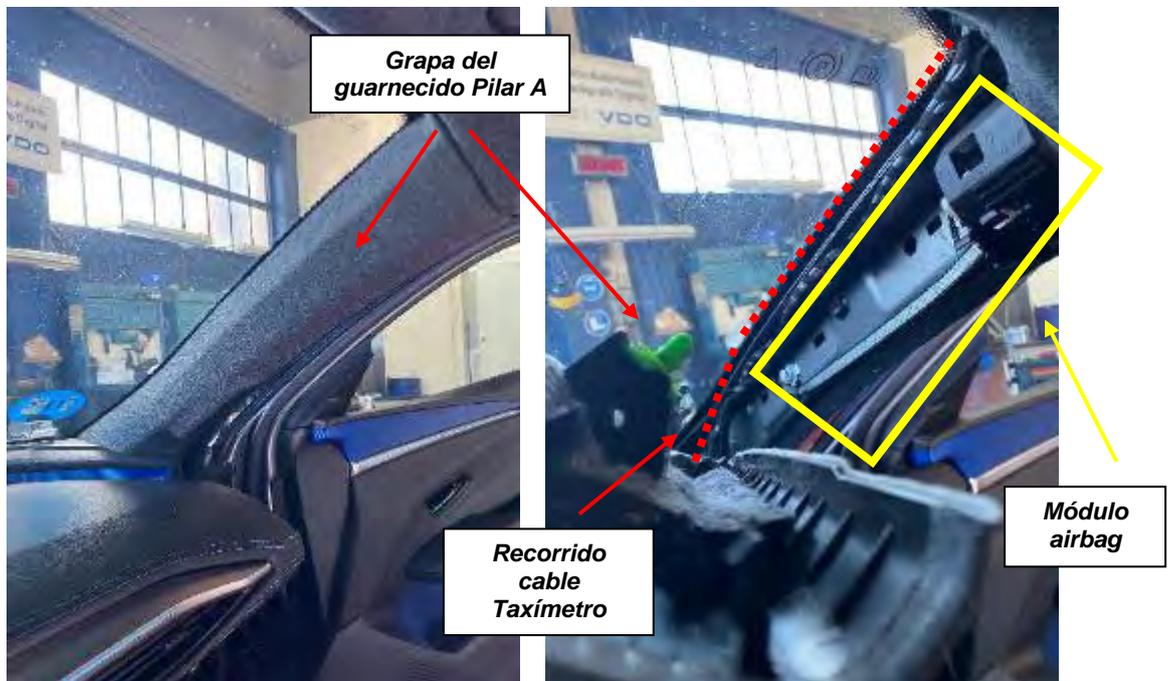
Detalle del desmontaje del pilar A.
